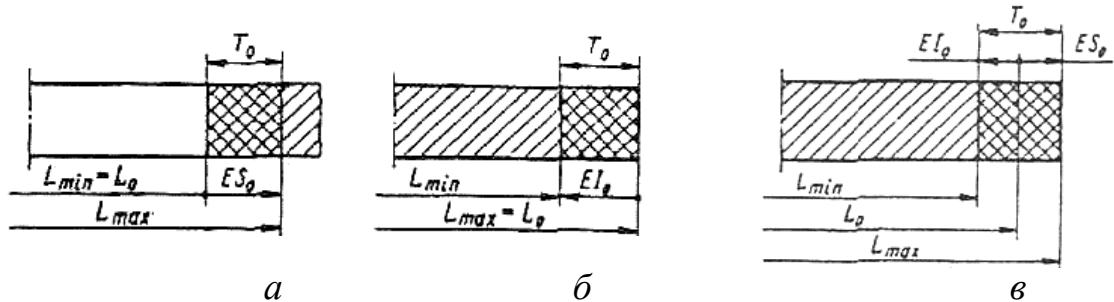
Можливі варіанти розташування полів допусків для розмірів виливки: T_0 – допуск на розмір виливки; ES_0 – верхнє відхилення; EI_0 – нижнє відхилення.
